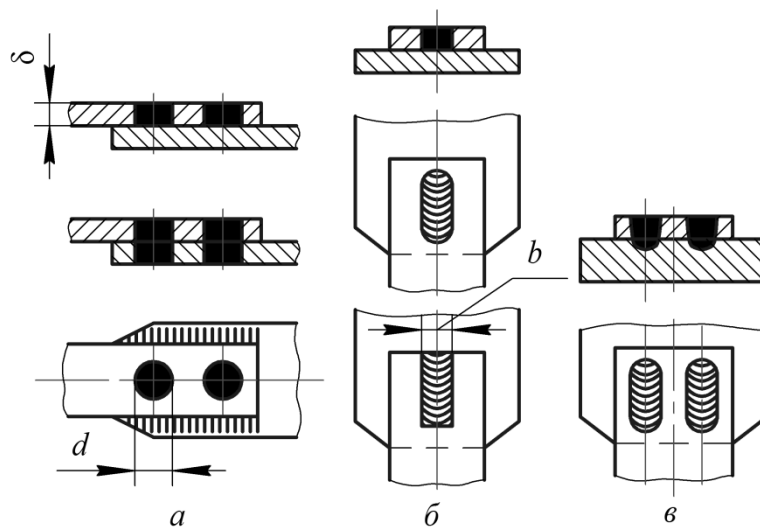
Пробочные, прорезные, проплавные сварные соединения
